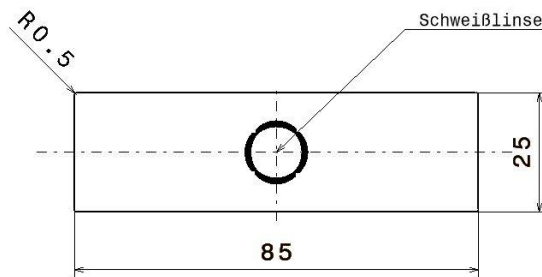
Probengeometrie Schweißproben. Es wurden jeweils zwei Bleche der Größe 25x85mm übereinander gelegt und mittels Widerstandspunktschweißen miteinander verbunden.
